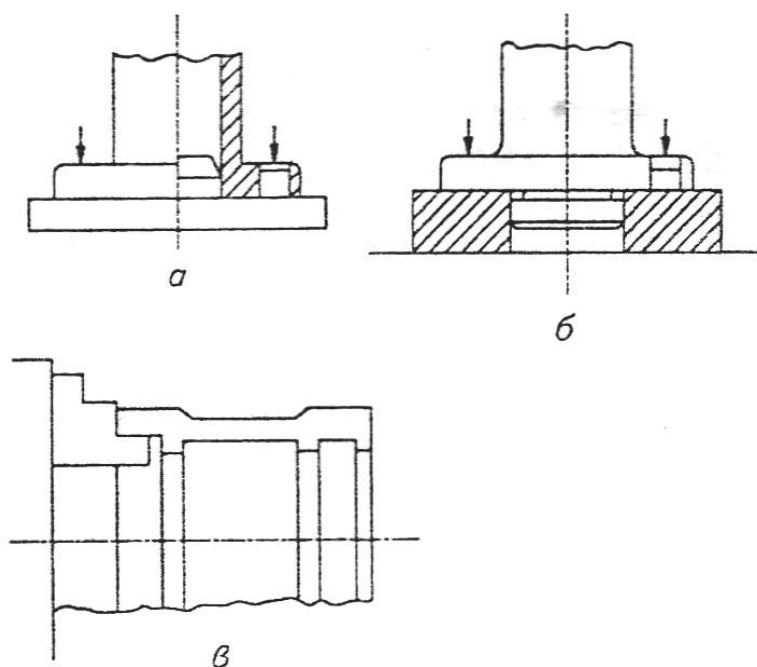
Схемы базирования фланцевых корпусных деталей: а, б, в – варианты
